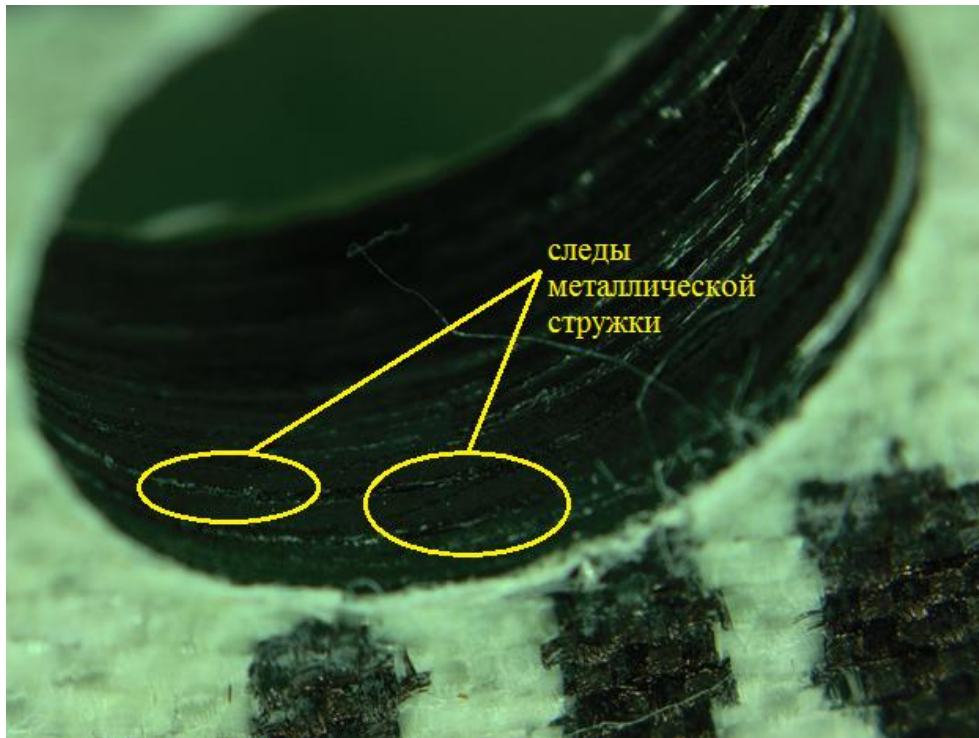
Повреждения на обработанной кромке пластины из ПКМ при сверлении пакета металл-композит-металл
